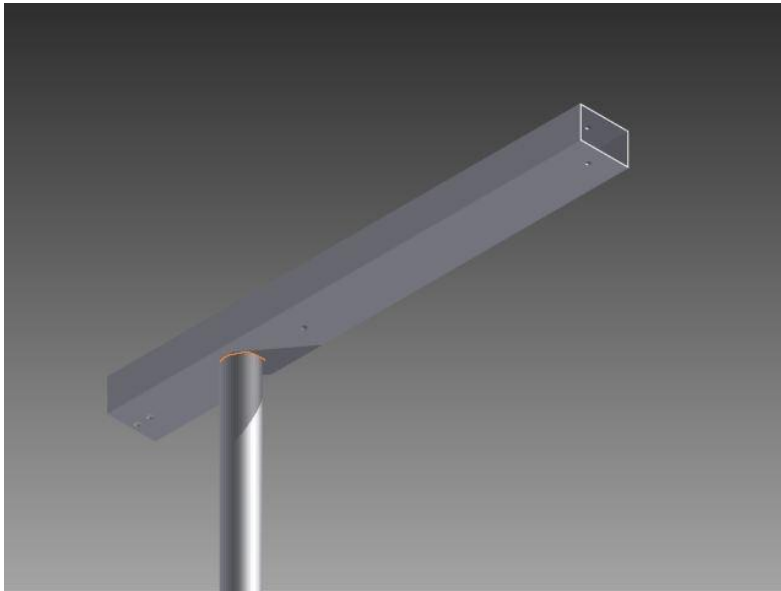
Unión soldada entre el PTR y el tubo mecánico
